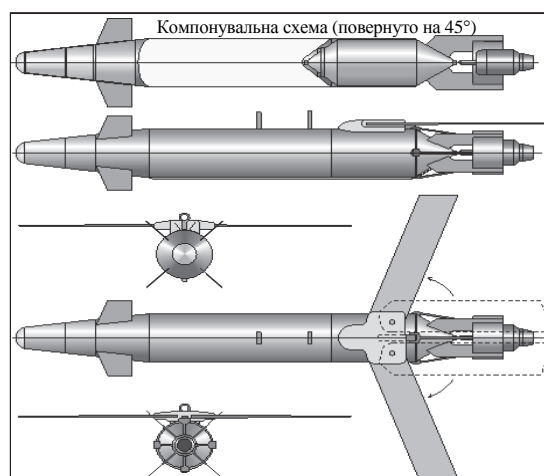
Компонувальна схема і загальний вигляд КАБ
